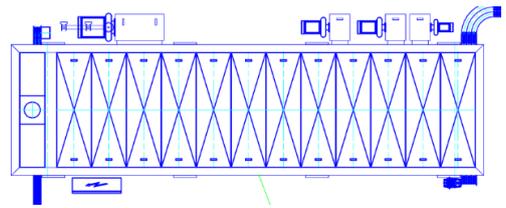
Tunnel del trattamento termico a pioggia in pianta
